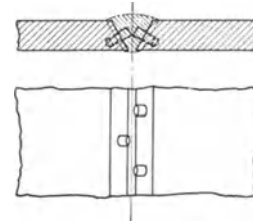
Sicherung der Schweißnaht durch Stiftschrauben.
